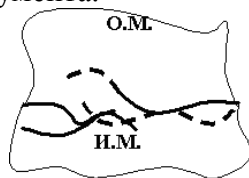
Абразивное изнашивание: О.М – обрабатываемый материал; И.М. – инструментальный материал.
